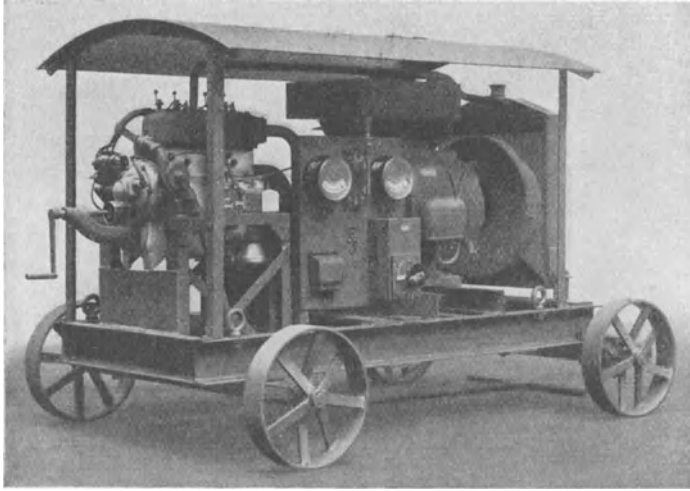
Fahrbarer Gleichstromschweißumformer mit Benzinmotorantrieb.
